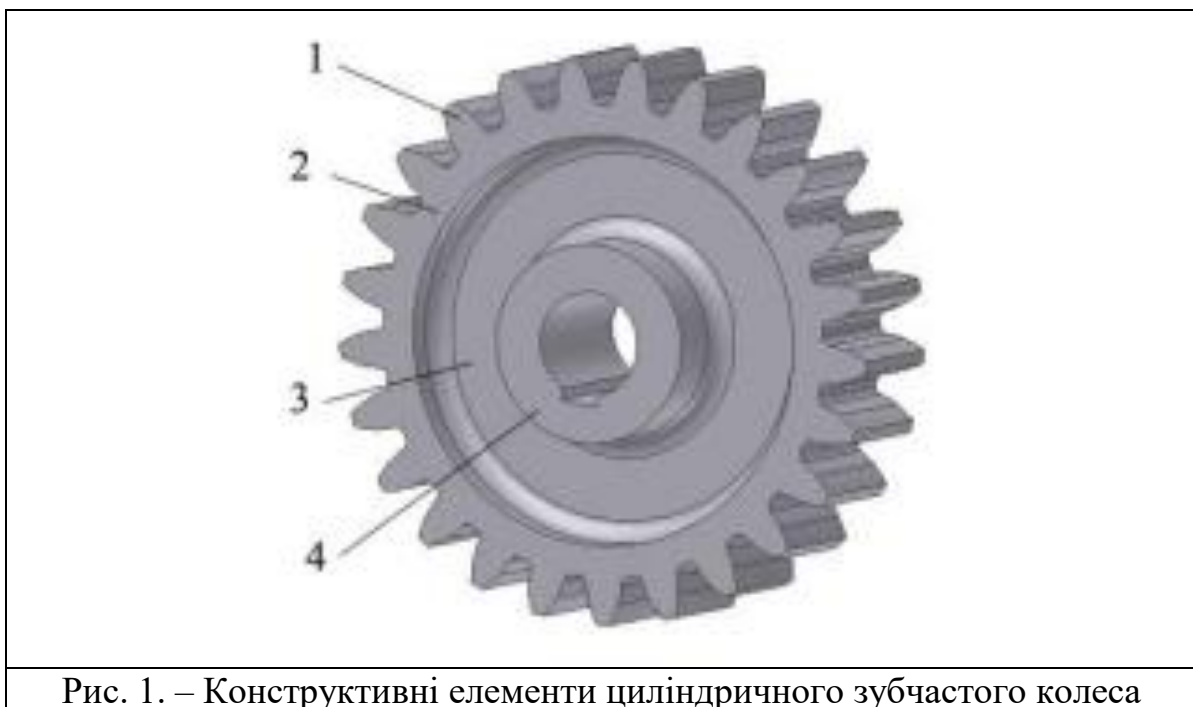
Конструктивні елементи циліндричного зубчастого колеса
